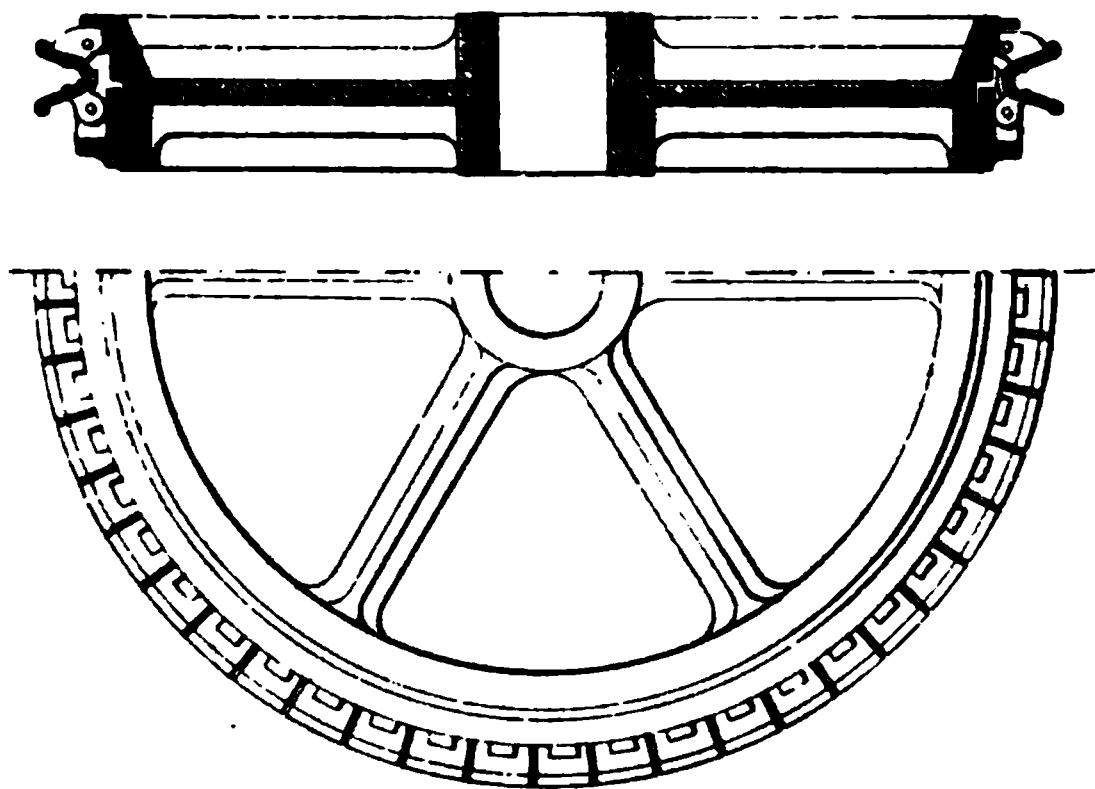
et 430. Poulie Fowler (coupe et plan).
